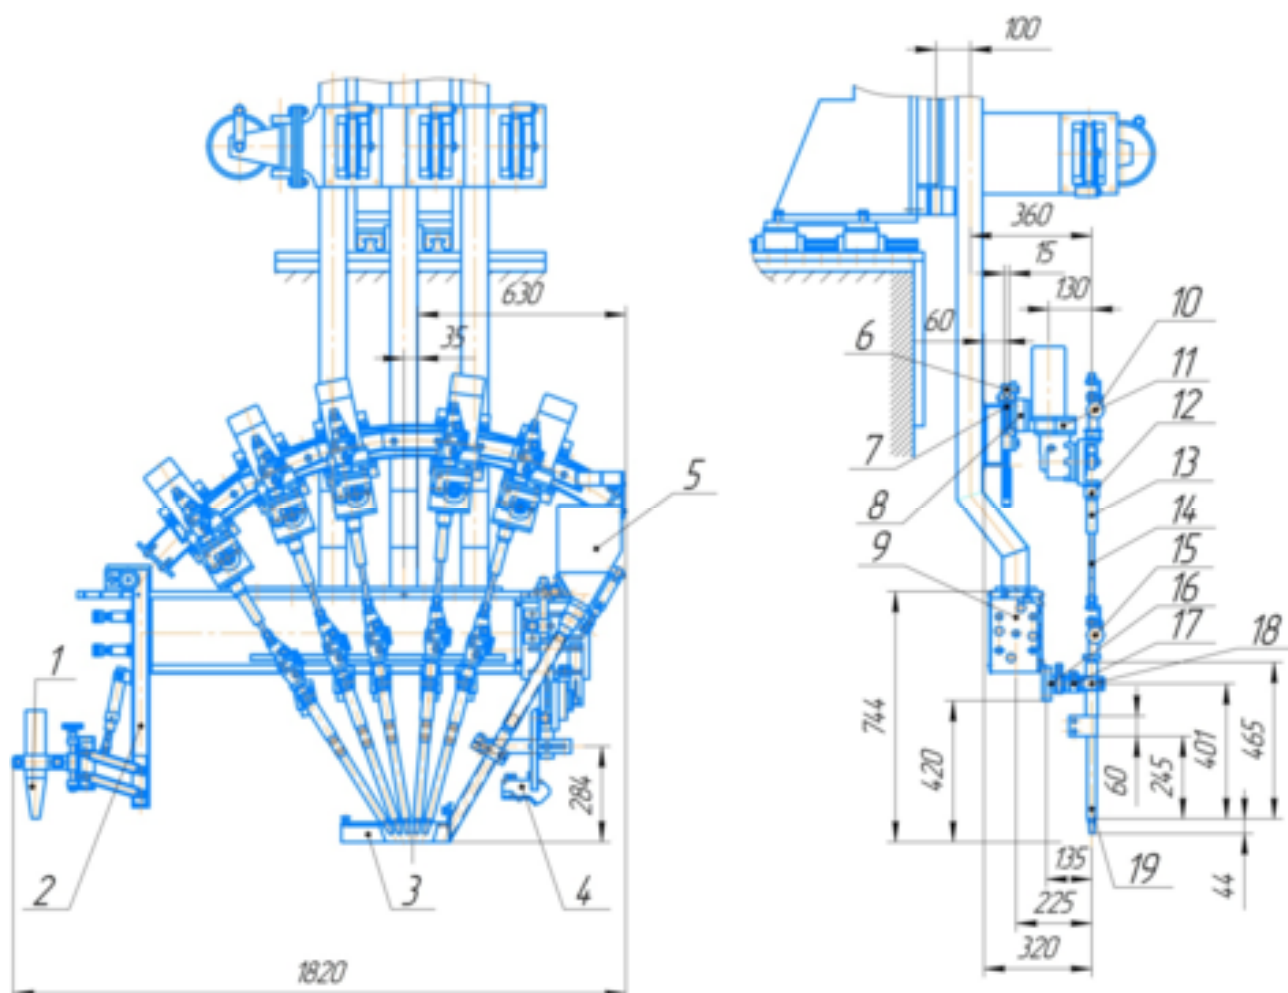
Головка сварочная пятидуговая:
